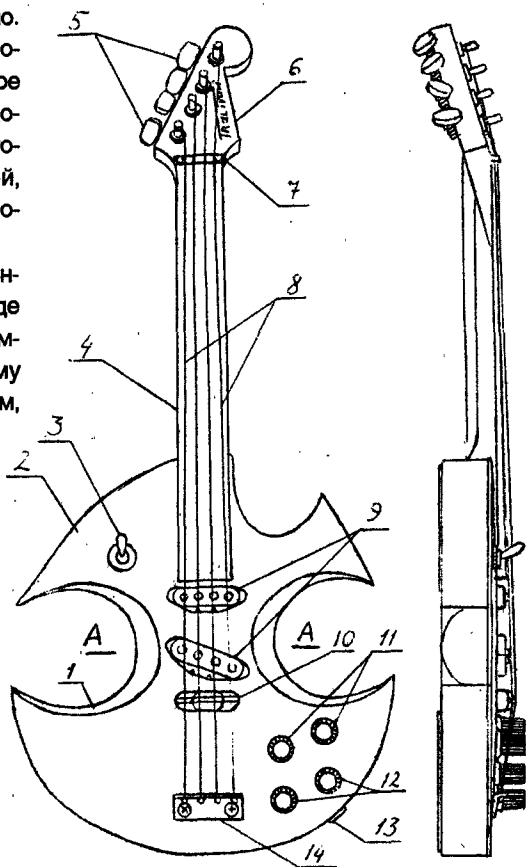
Смычковый ЭМИ: 1 - корпус; 2 - дека; 3 - переключатель; 4 - гриф; 5 - колки; 6 - головка грифа; 7 - верхний порожек; 8 - струны; 9 - звукосниматели; 10 - нижний порожек; 11 - регуляторы уровня (R2, R4); 12 - регуляторы тембра (R1, R3); 13 - выходное гнездо; 14 - струнодержатель
